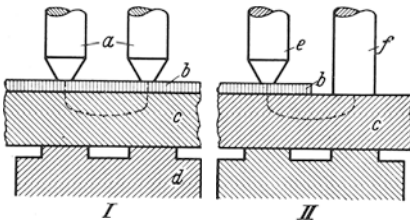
Schema der Doppelpunktschweißung.
